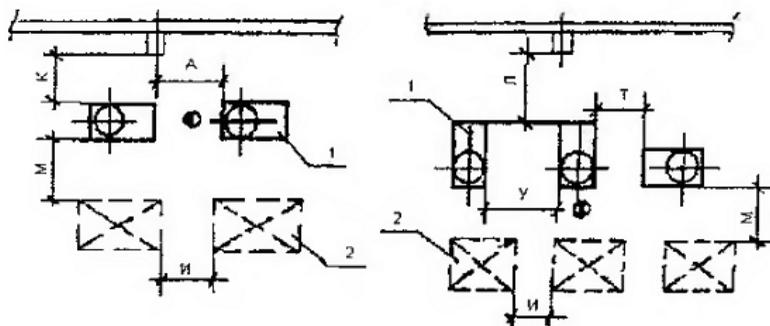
Размещение автоматов для сварки кольцевых швов: 1 - сварочный автомат; 2 - место складирования
